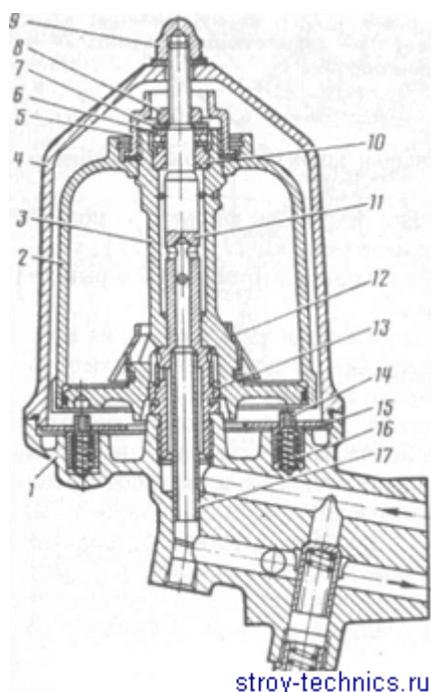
Центробежный масляный фильтр двигателя КамАЗ-740:
